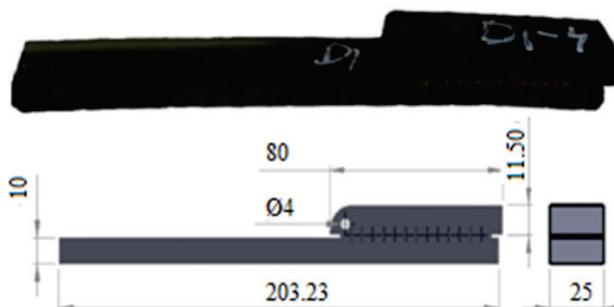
Ezme test düzeneği (The crush decohesion test assembly)
